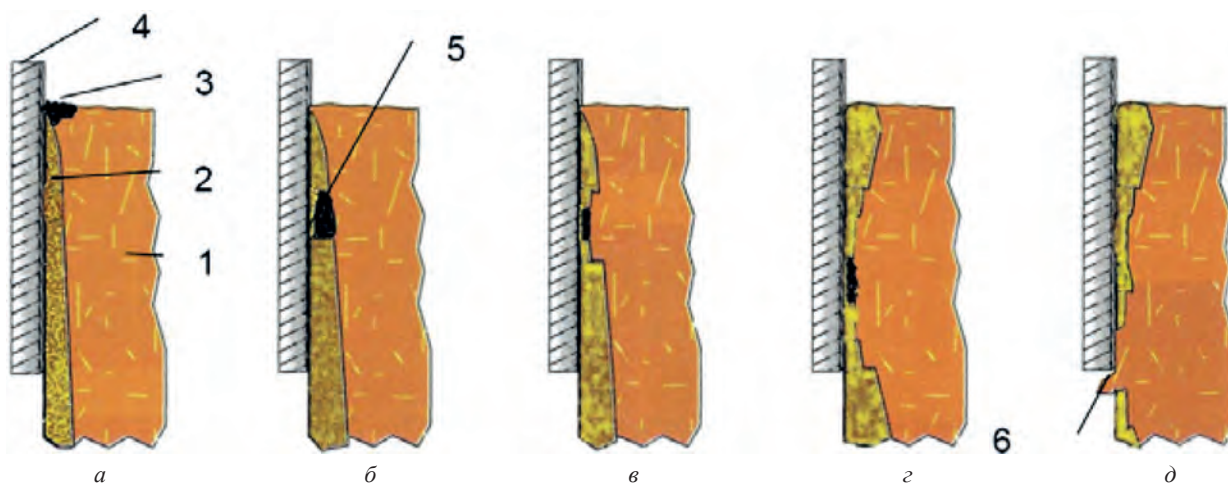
Схема образования шлакового прорыва из-за твердых включений на мениске металла: 1 – жидкий металл; 2 – корочка металла; 3 – конгломератное включение на мениске металла; 4 – кристаллизатор; 5 – дефектная корочка с оксидным конгломератом; б – прорыв металла под кристаллизатором на выходе дефектной корочки из кристаллизатора
